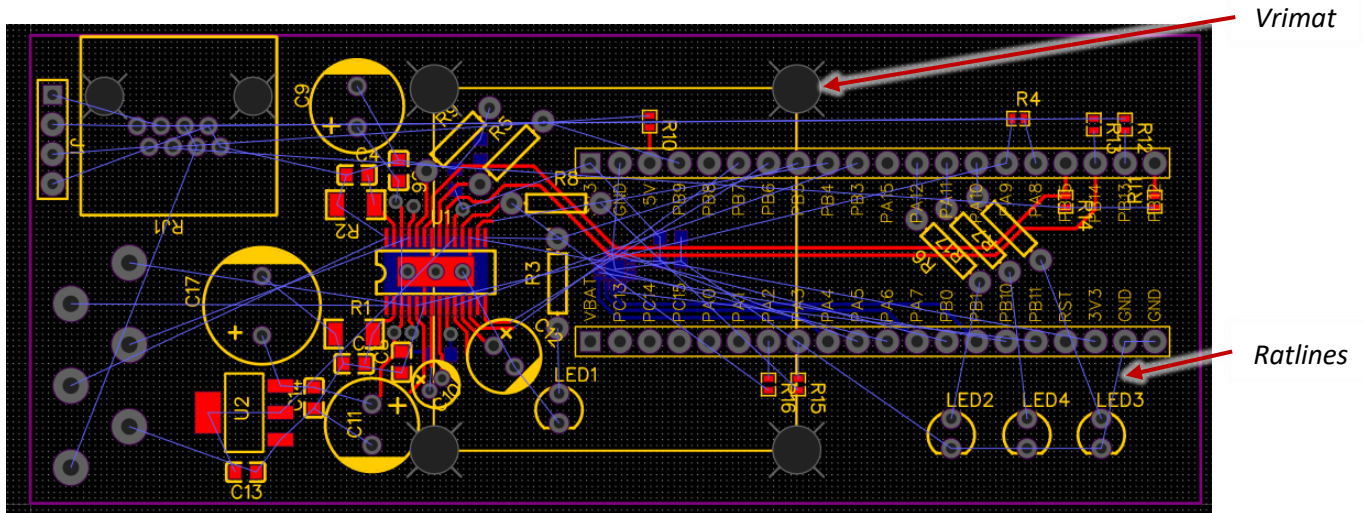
Realizimi i lidhjeve të komponentëve në PCB
